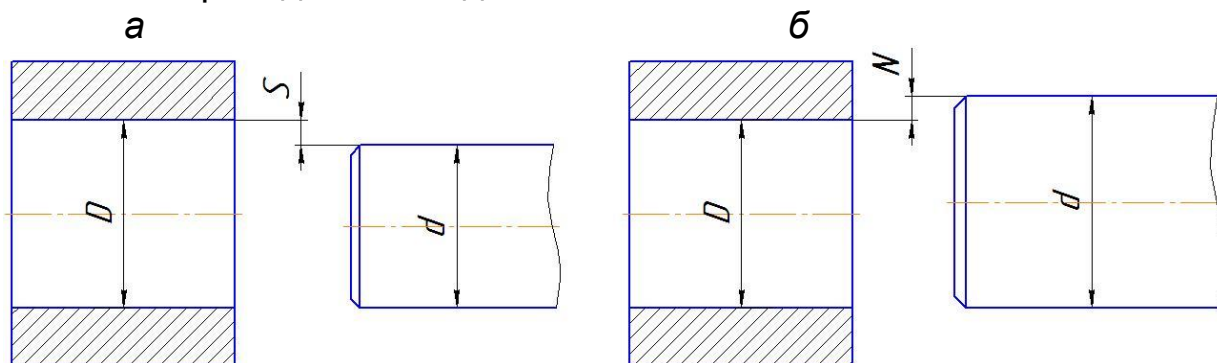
Схема образования зазоров и натягов в соединении вал – втулка
